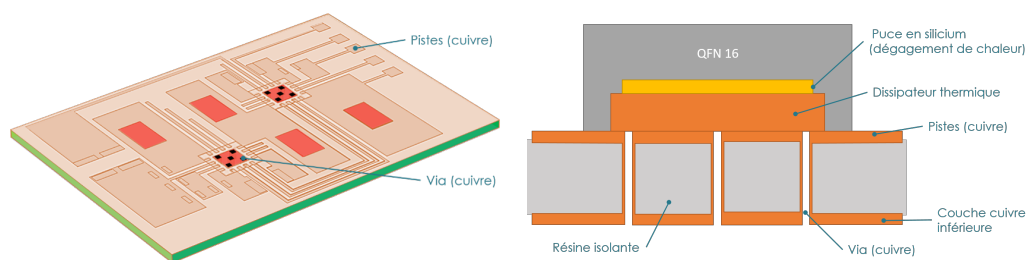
Géométrie du PCB. À gauche, plan des pistes et à droite, coupe de principe du PCB
